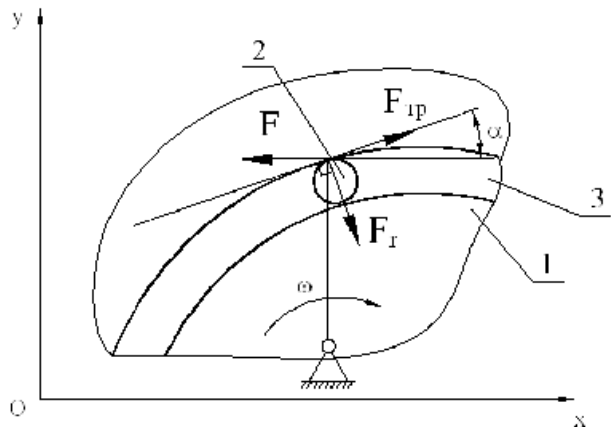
Розрахункова схема системи передачі вимірювального приладу: 1 – зубчате колесо; 2 – штифт; 3 – паз зубчатого колеса
